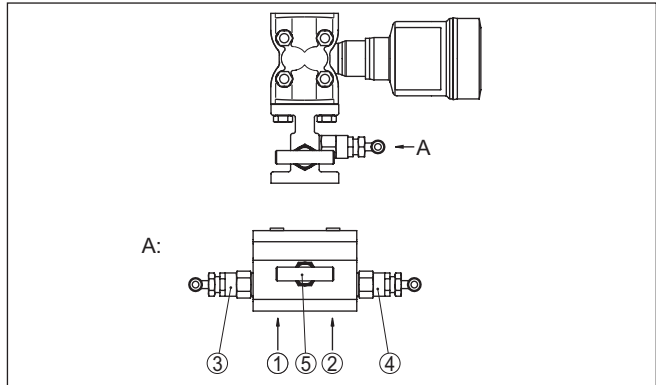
Conexão de um bloco de 3 válvulas com flange em ambos os lados
